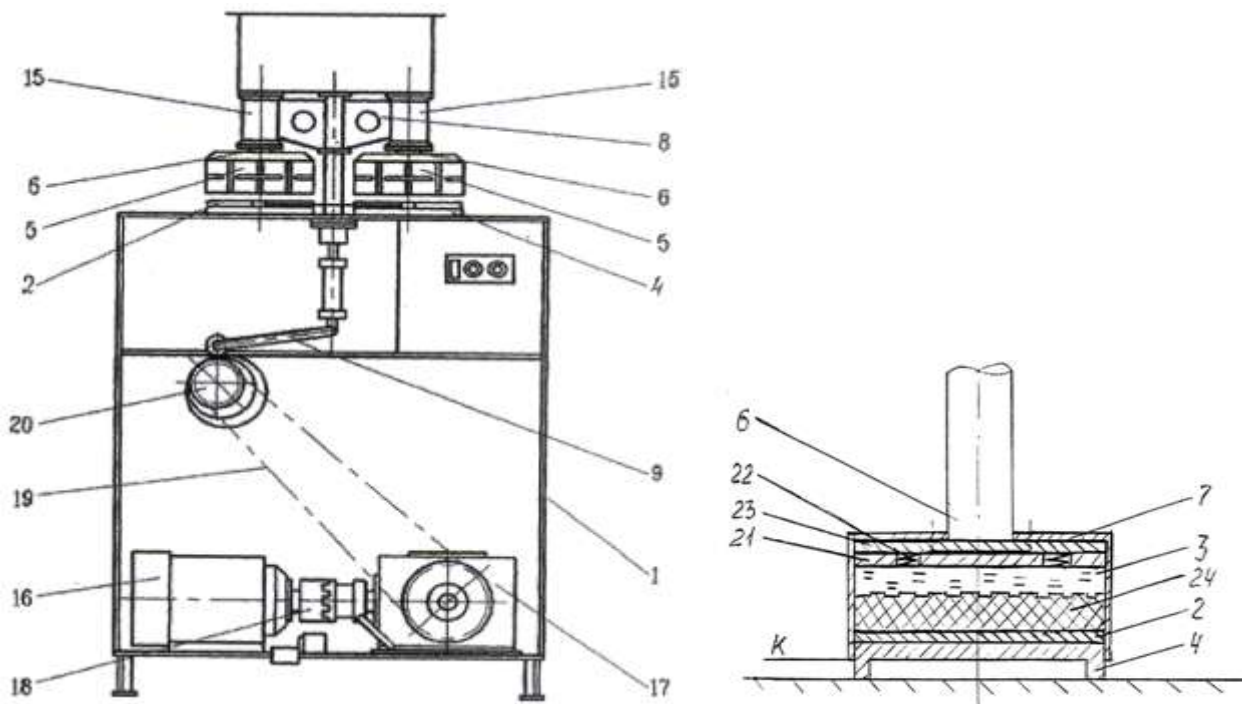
Установка для формования и печатания тестовых заготовок пряников
